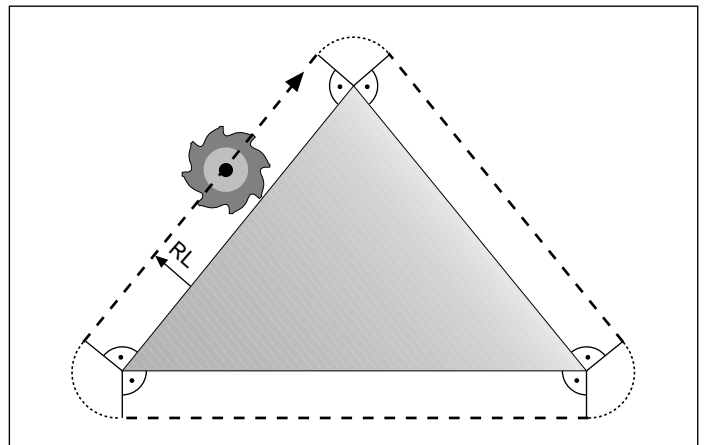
Werkzeug wälzt sich an Außenecken ab
